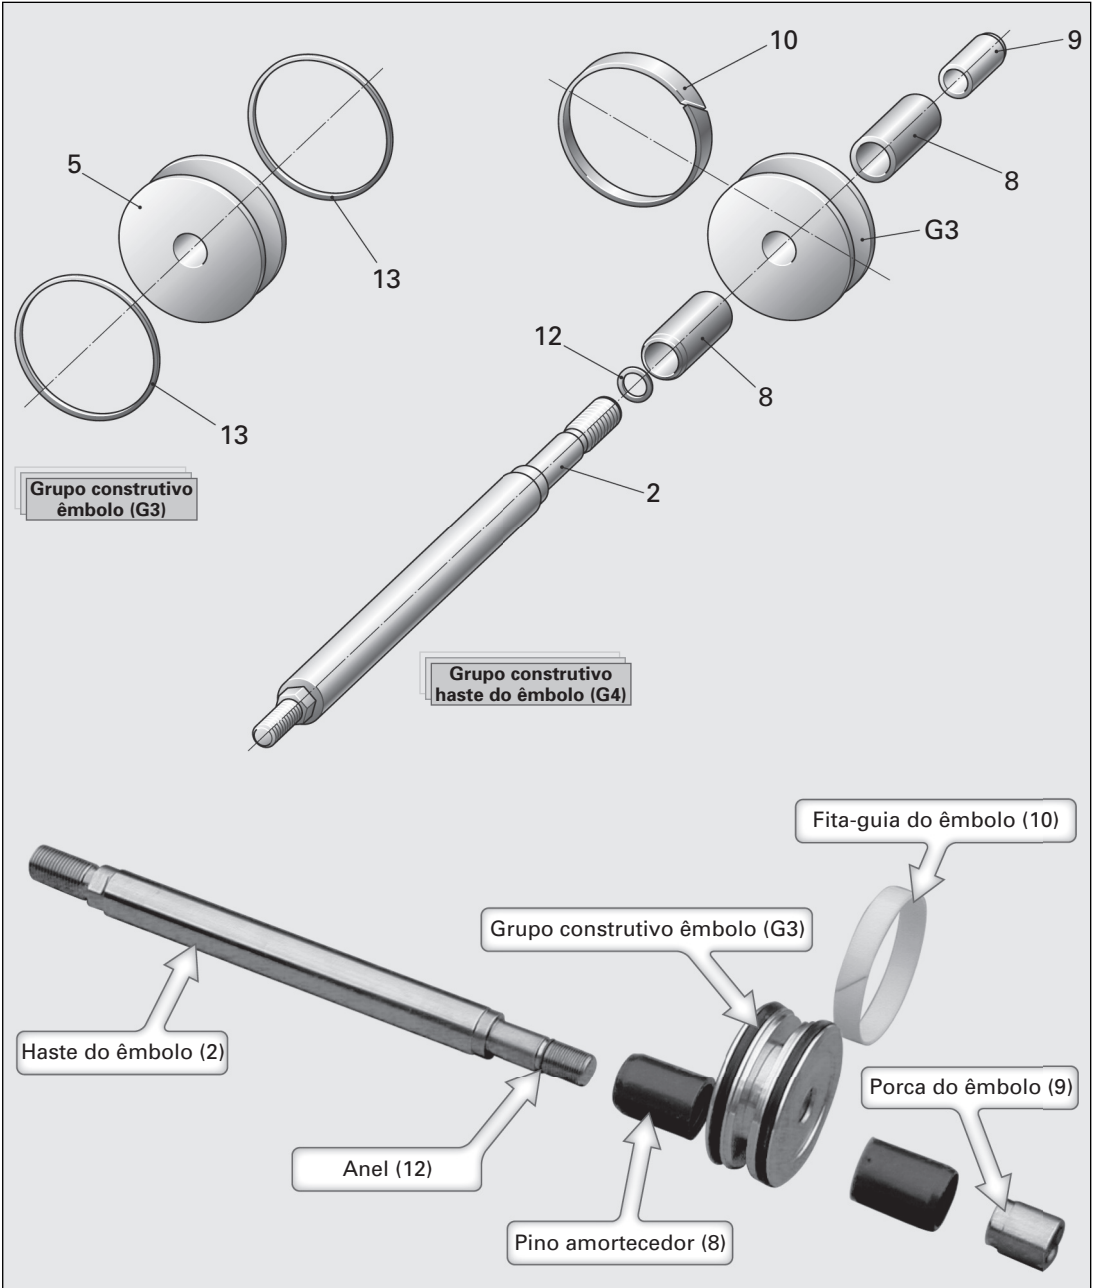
Grupos construtivos êmbolo e haste do êmbolo
